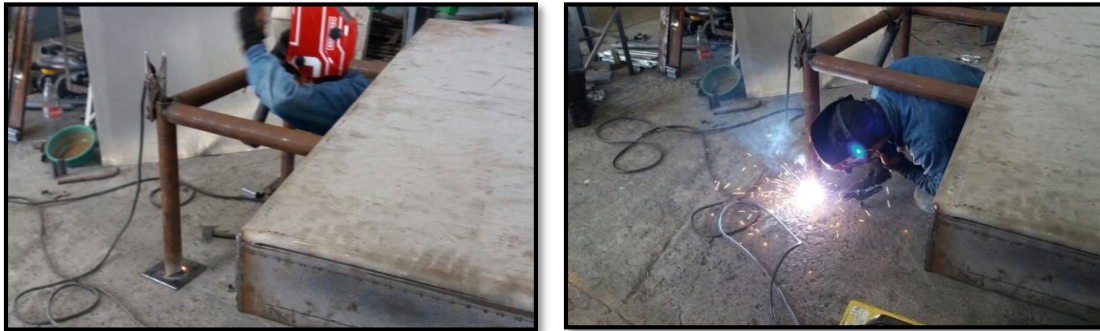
Soldadura de láminas de estructura de soporte. Fuente: Autores
